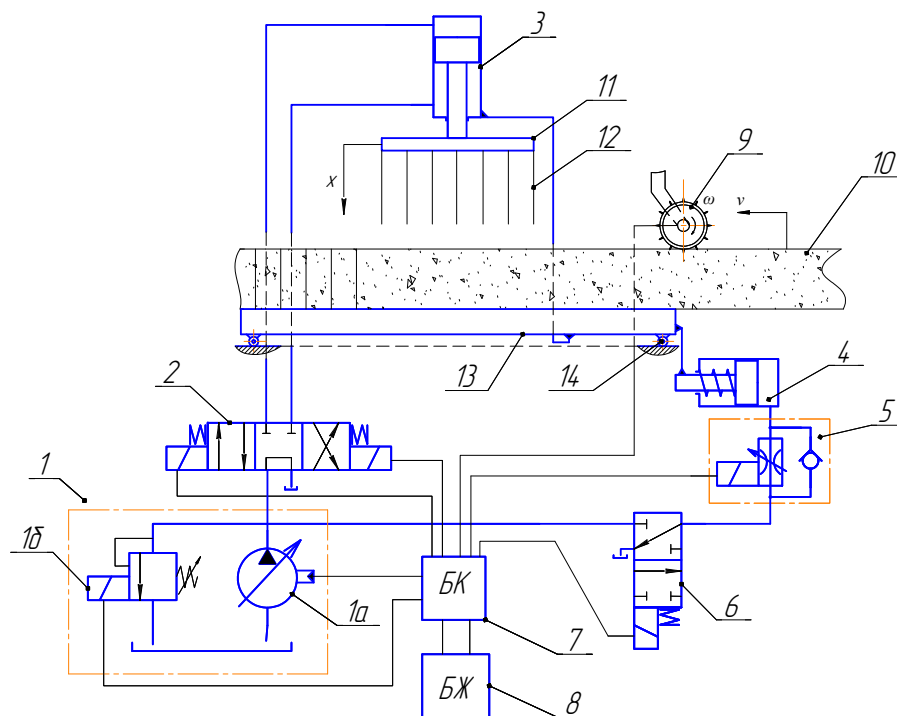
Функціональна схема автоматизованого пристрою для формування заготовки цегли
